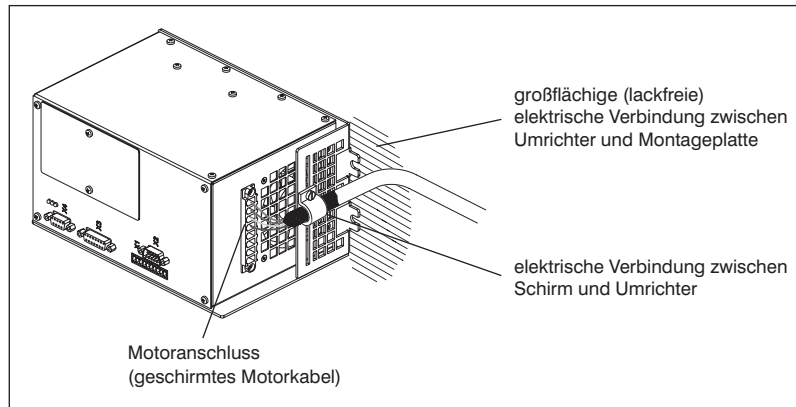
EMV-gerechter Aufbau auf Montageplatte (Motoranschluss)
